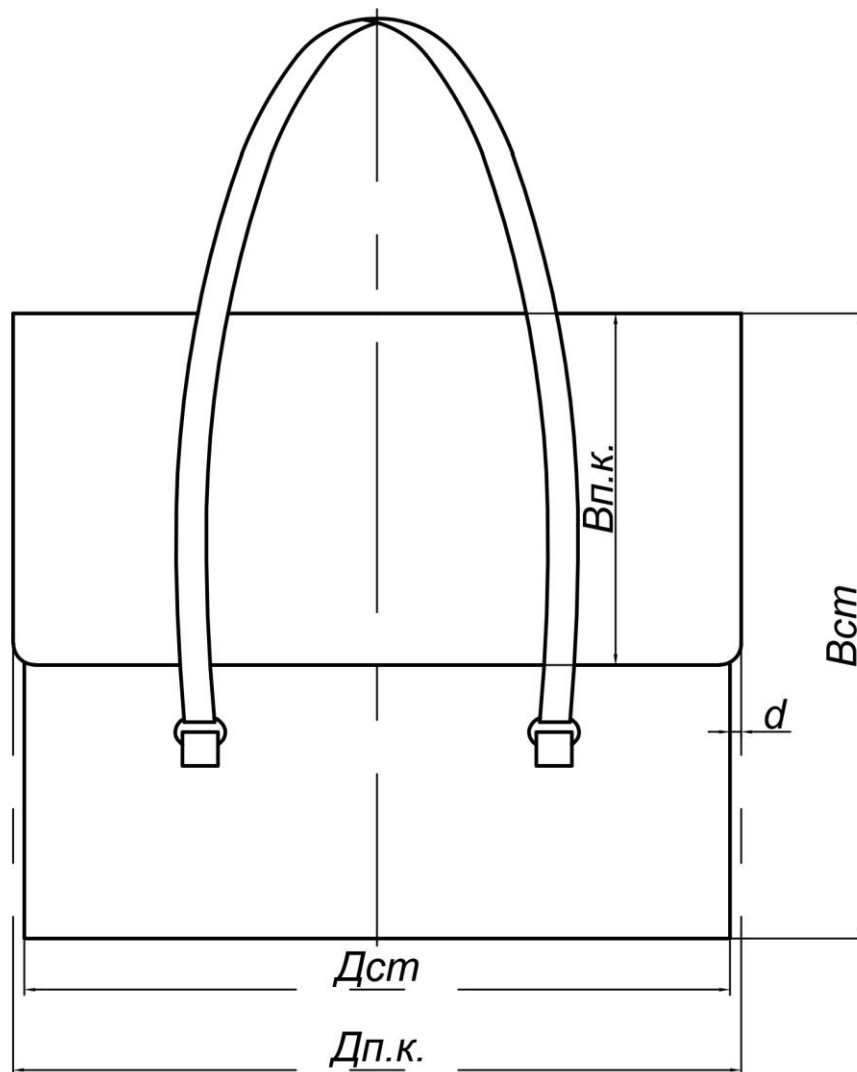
Размеры деталей сумки, закрывающейся на клапан
